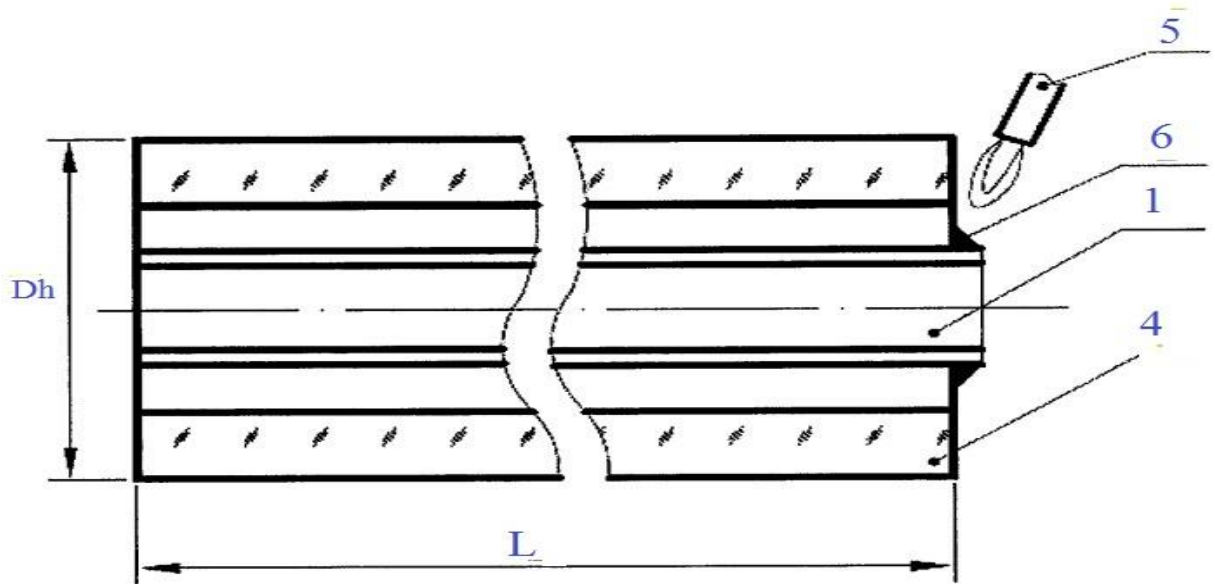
Схема сплавления стержня-заготовки и кварцевой трубы
